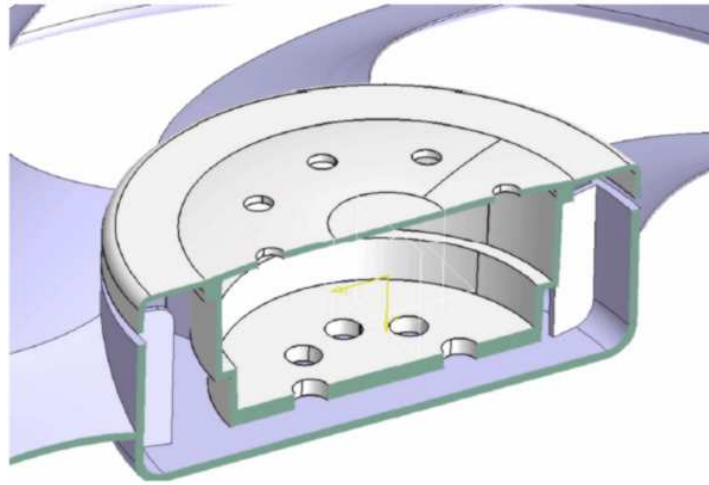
Conjunto para calculo del ventilador y parte exterior del motor
